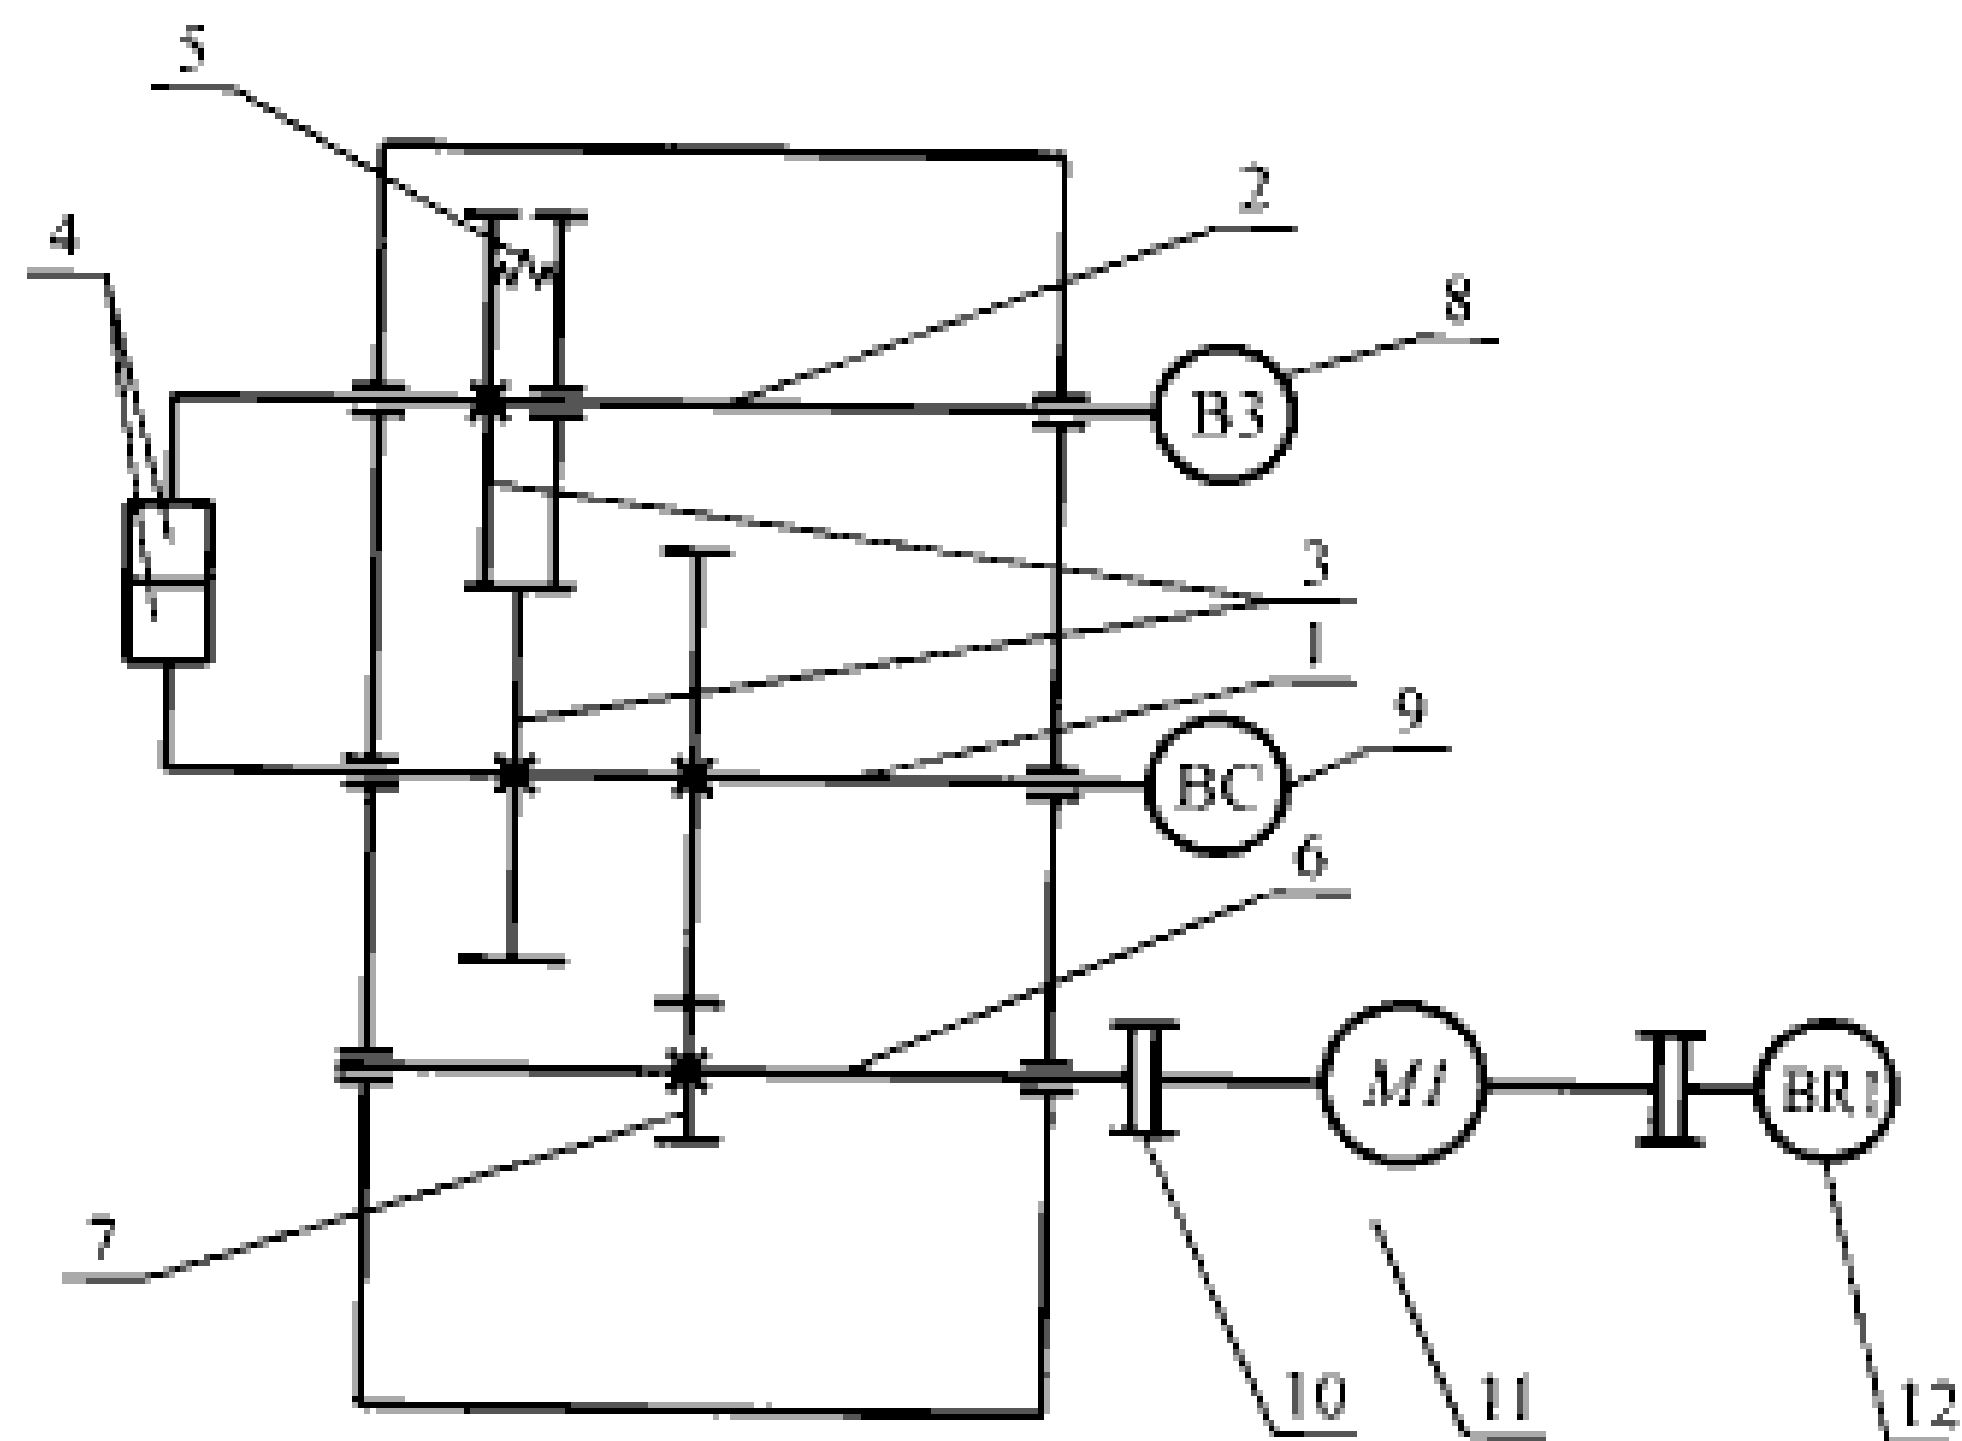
Кинематическая схема станка для мерной разрезки проката:
